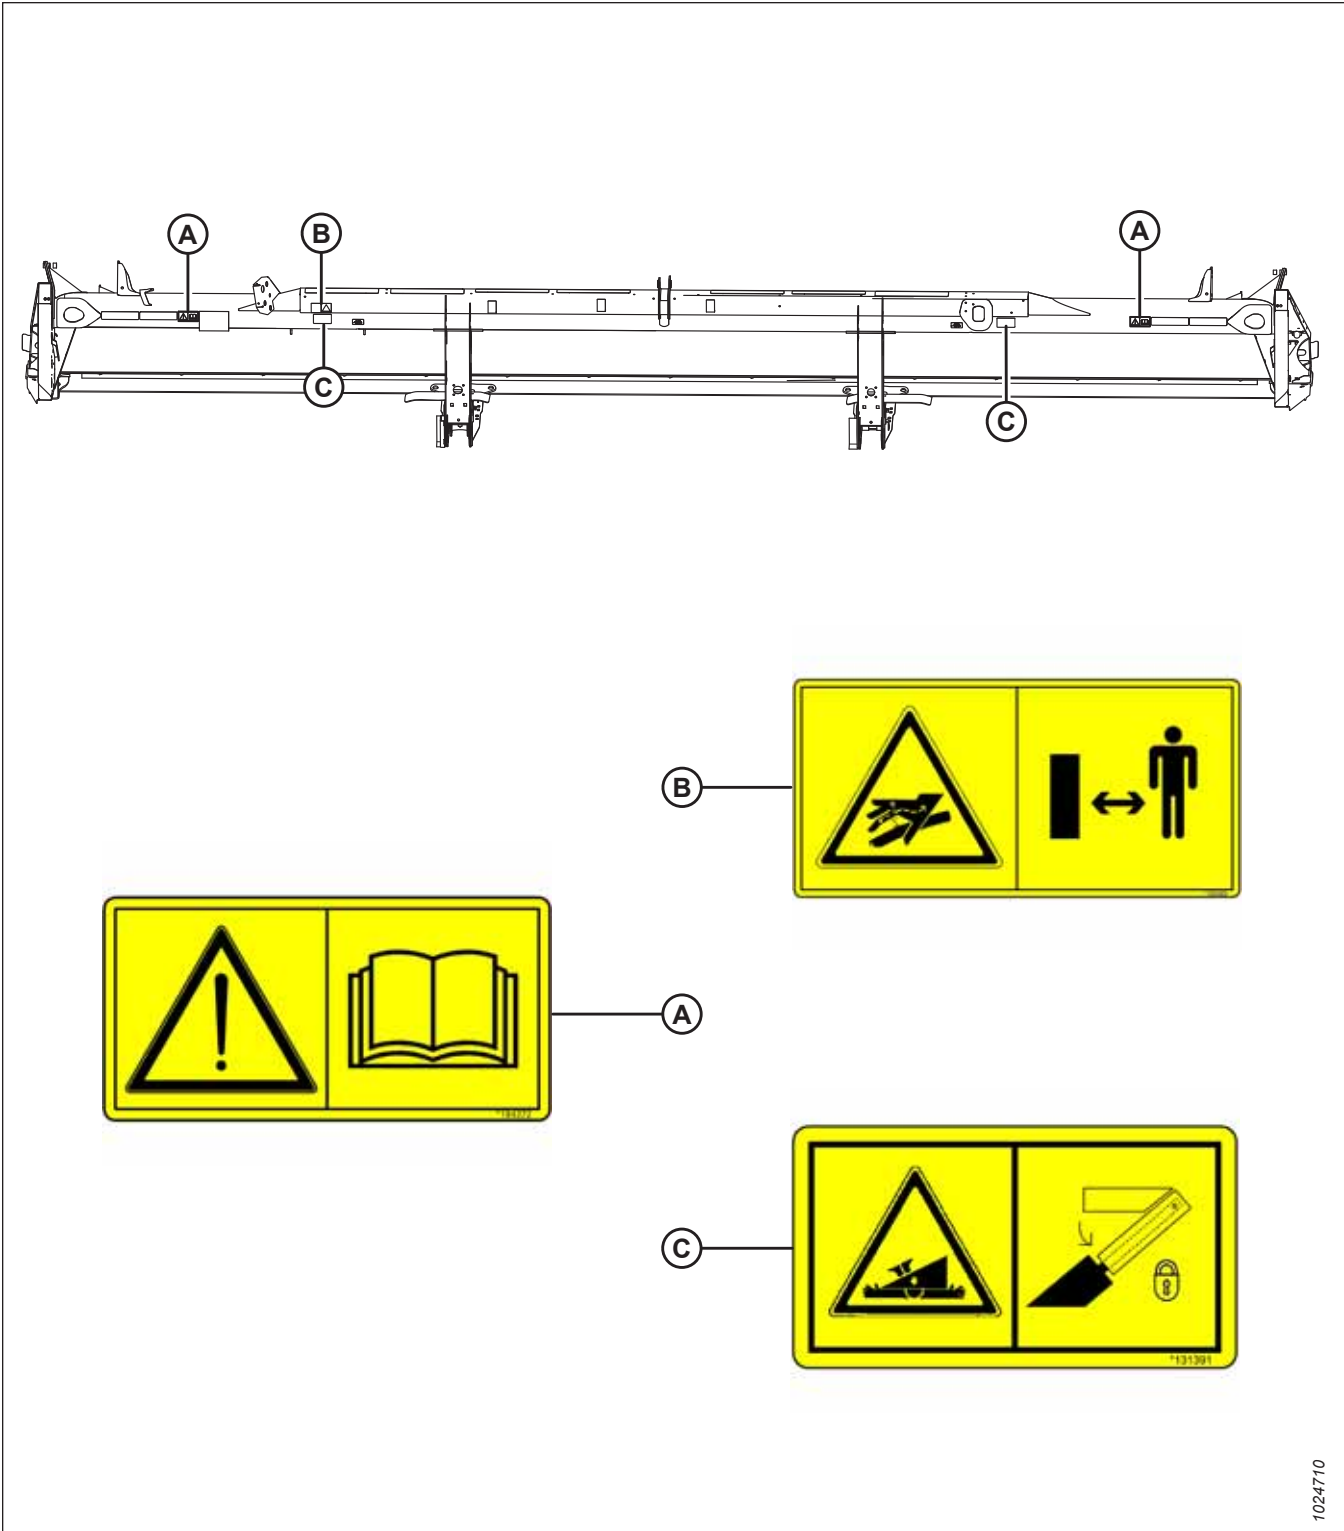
Tube arrière – Plateforme rigide de 7,6 m (25 pi)
